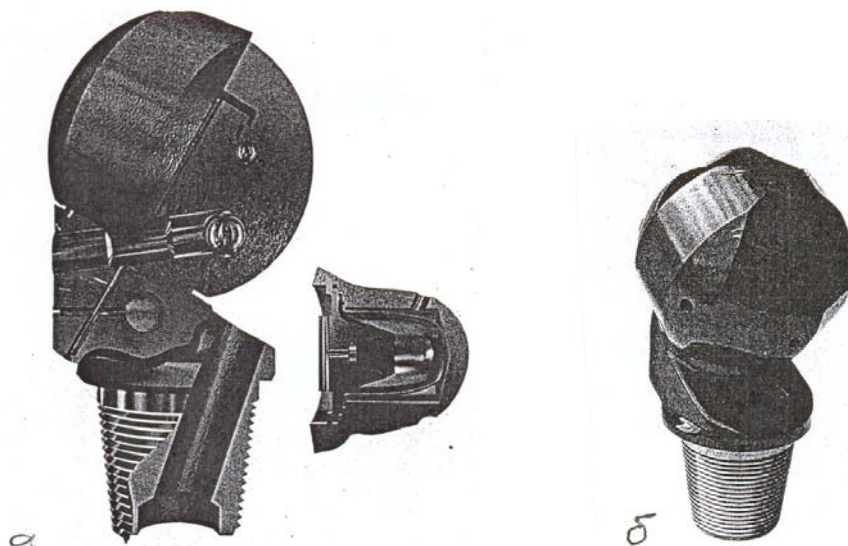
Разрез и общий вид развальцевателя ОРШ
